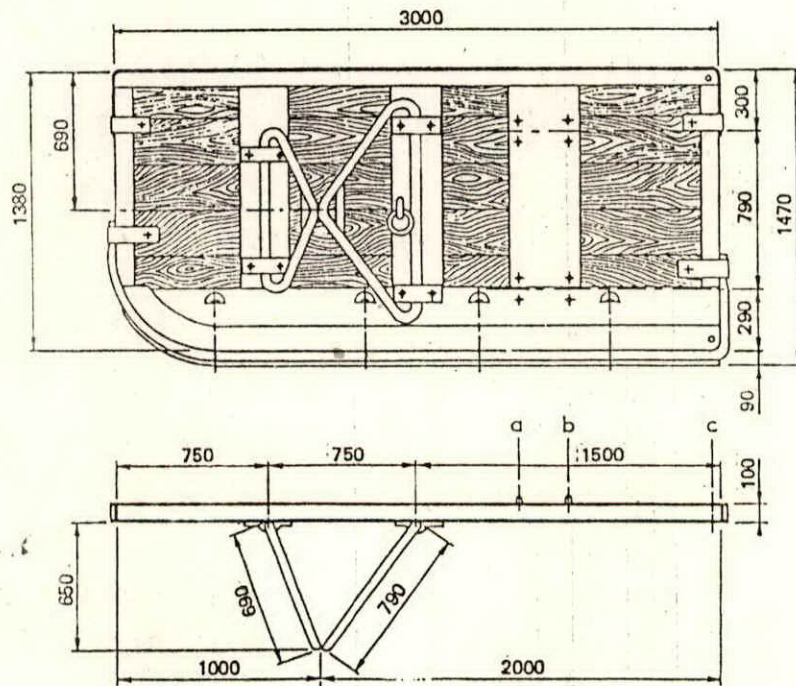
Panneau rectangulaire plan. Proportions générales.
